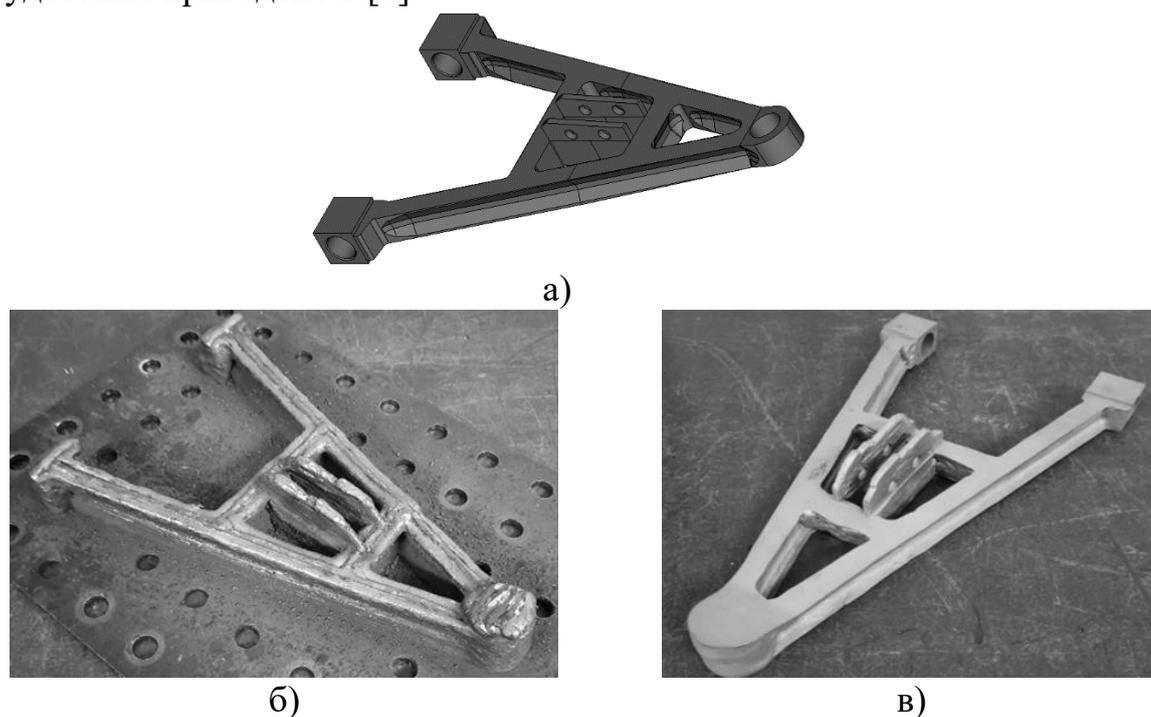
3D-модель (а), напечатанная заготовка (б) и деталь «Рычаг» (в) после обработки.
